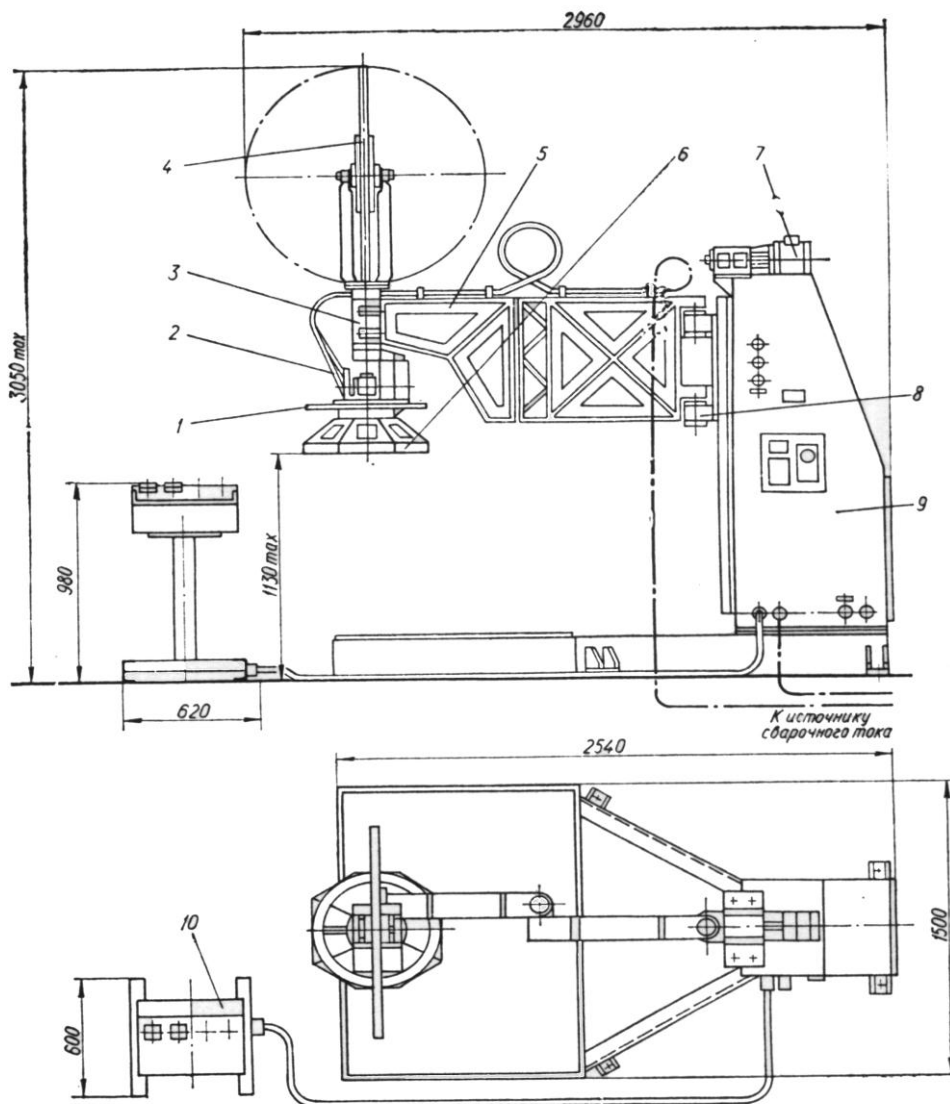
Полуавтомат А-1728 для дуговой наплавки порошковой лентой
